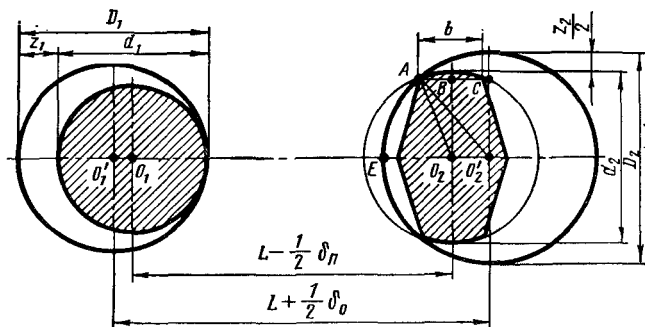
Расчетная схема для случая установки заготовки на цилиндрический и срезанный пальцы:
